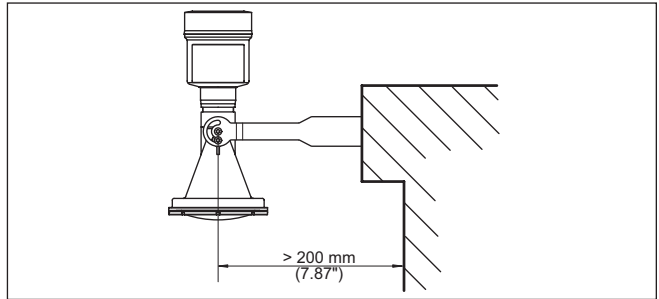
Wandmontage waagrecht über den Montagebügel mit Länge 170 mm
